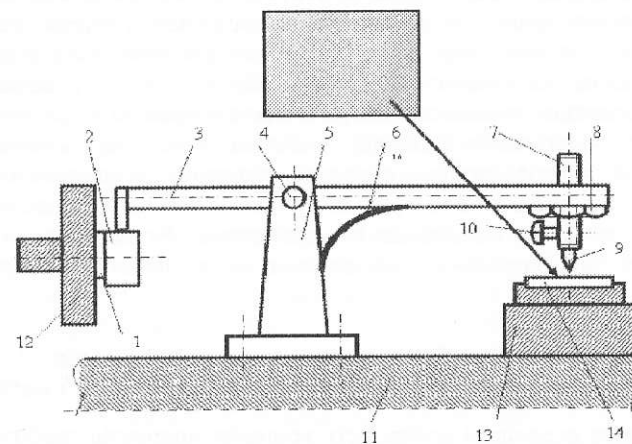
Пристрій для створення лунок: 1 – привідний вал; 2 – кулачок; 3 – коромисло; 4 – вісь коромисла; 5 – стояк осі коромисла; 6 – пружина; 7 – регульовальний гвинт; 8 – контргайка регульовального гвинта; 9 – бойок; 10 – механізм кріплення бойка; 11 – основа; 12 – патрон; 13 – механізм переміщення; 14 – деталь (зразок)
